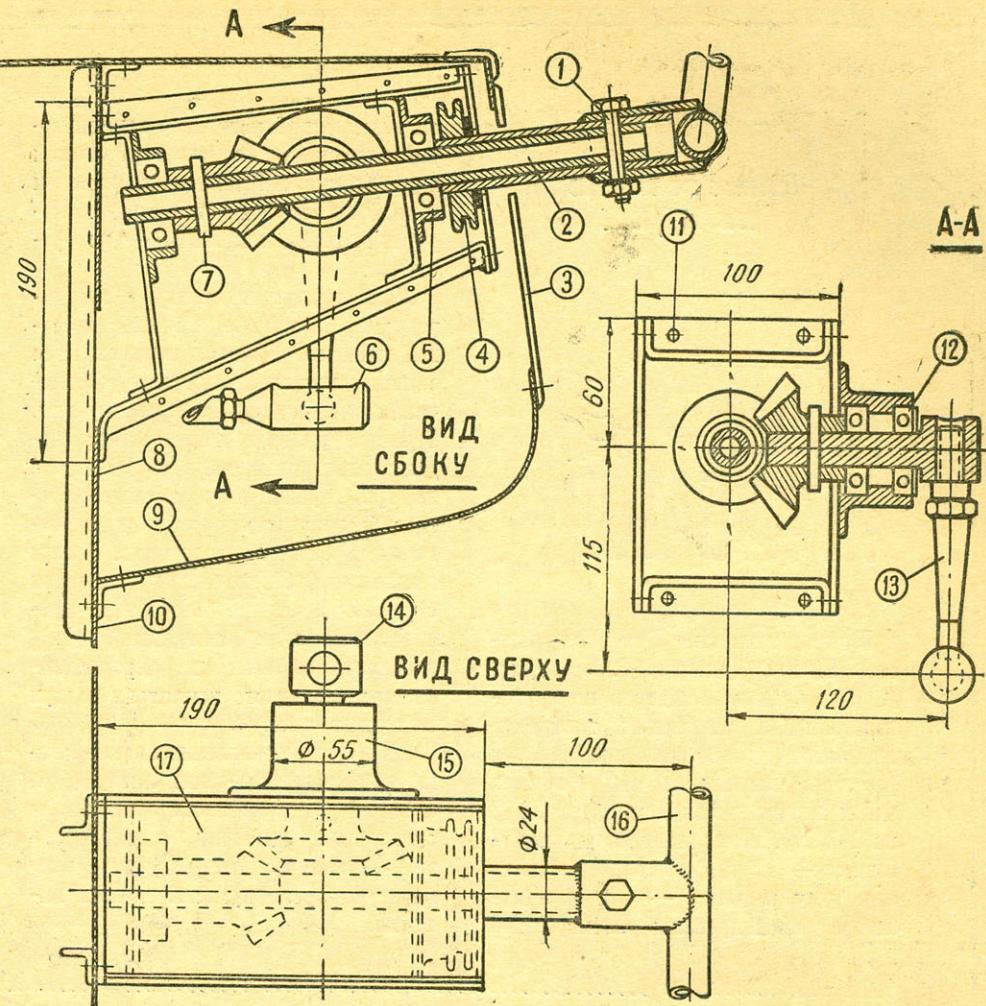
Рулевой механизм: 1 — стопорный болт; 2 — валик; 3 — приборный щиток; 4 — шкив; 5 — подшипник № 204; 6 — приборный щиток; 7 — наконечник рулевой тяги; 8 — рама № 4; 9 — обшивка багажника; 10 — силовой угольник; 11 — болт Ø 6 мм; 12 — подшипник № 204; 13 — специальный болт; 14 — валик; 15 — корпус подшипников; 16 — руль; 17 — корпус механизма.
